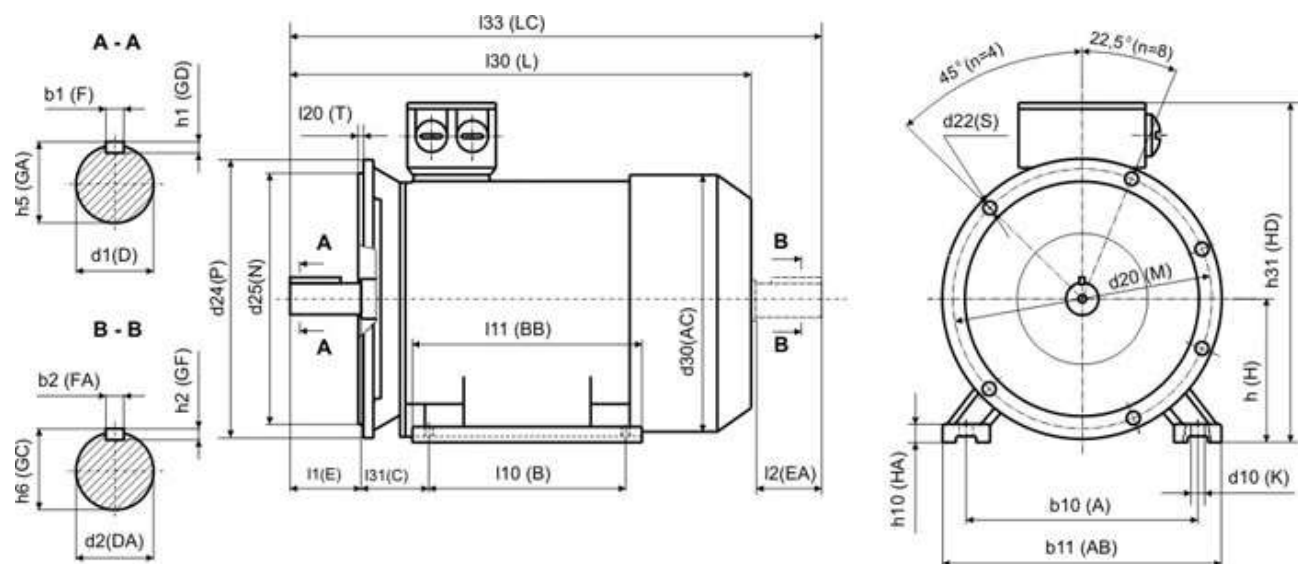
Габаритные и присоединительные размеры двигателя
